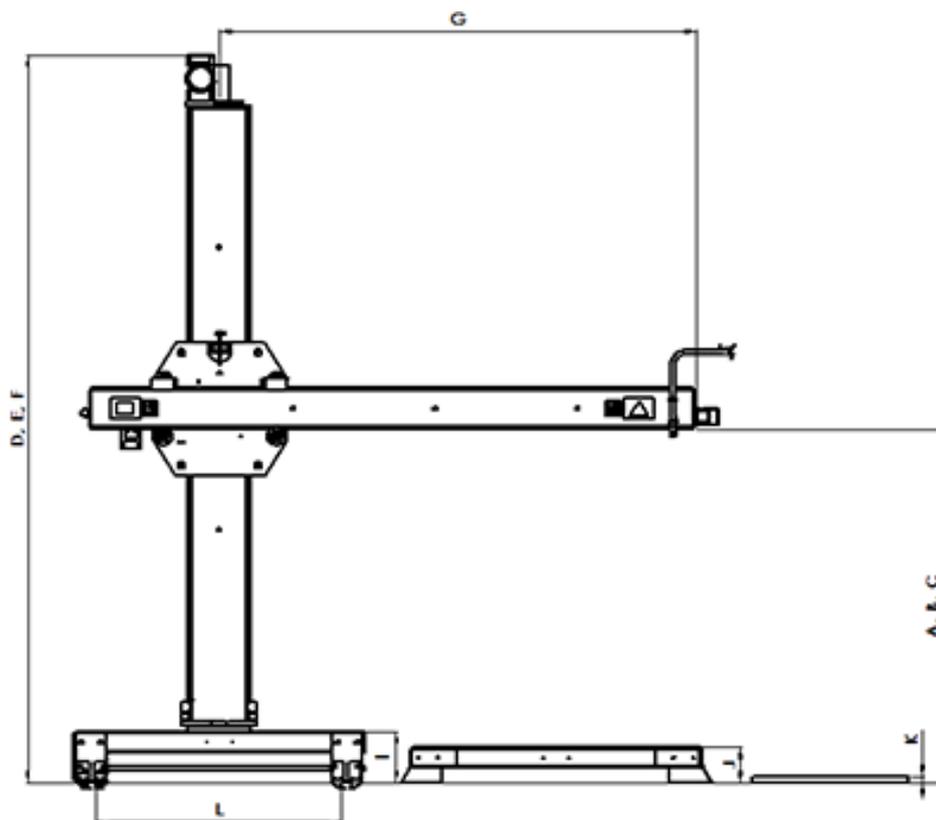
Сварочная колонна ESAB CaB 300S
